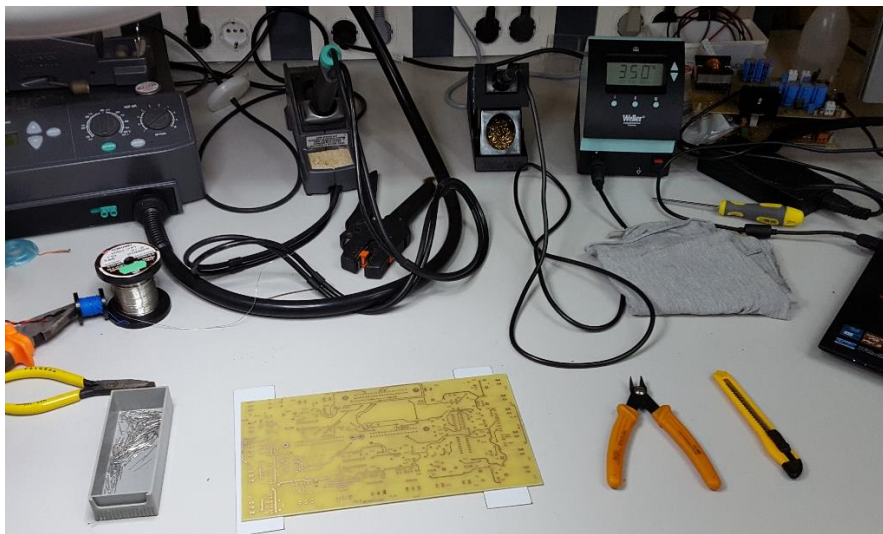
Estación soldadora y otros dispositivos empleados para soldar los componentes a la PCB
